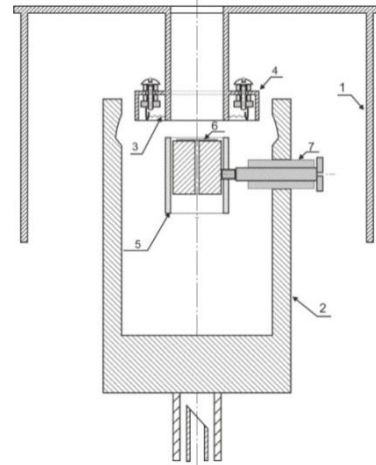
Схематичное изображение рентгеновской трубки в разрезе: 1 – кожух; 2 – анод; 3 – катод в виде кольца; 4 – торроидальный бокс прямоугольного сечения; 5 – образцедержатель; 6 – образец; 7 – керамические трубчатые изоляторы
